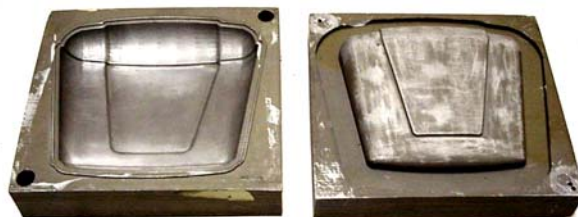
Molde em epóxi (Cast It 2000™) utilizado no processo de moldagem por compressão.
